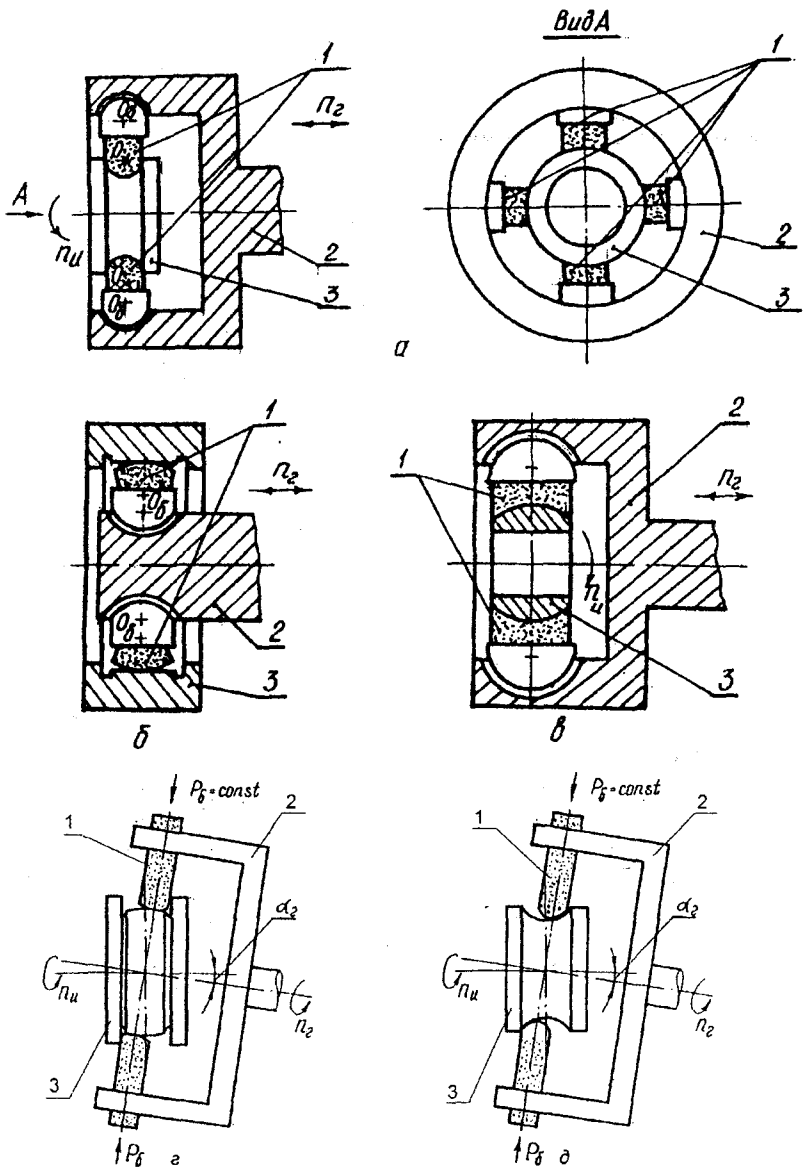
Схемы многобрусковой доводки рабочих поверхностей колец подшипников качения
